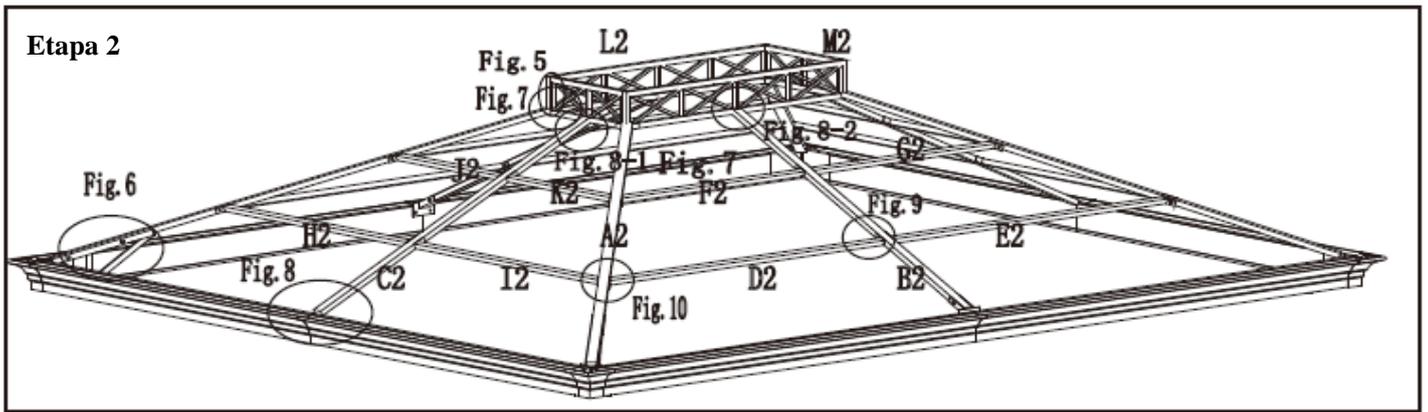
Conecte las vigas fijadas con la siguiente respectivamente y fije con tornillo (JJ) y arandela plana (BB).
